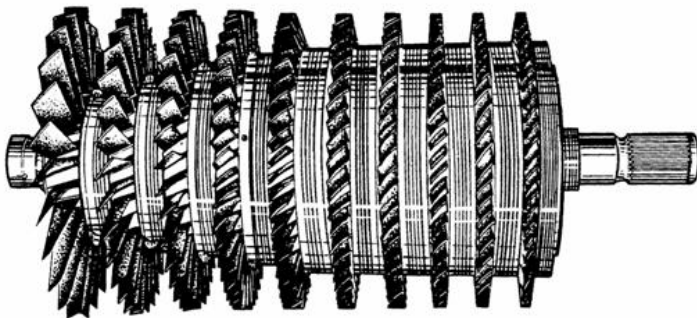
Зовнішній вигляд ротора компресора газотурбінного двигуна АІ-20
